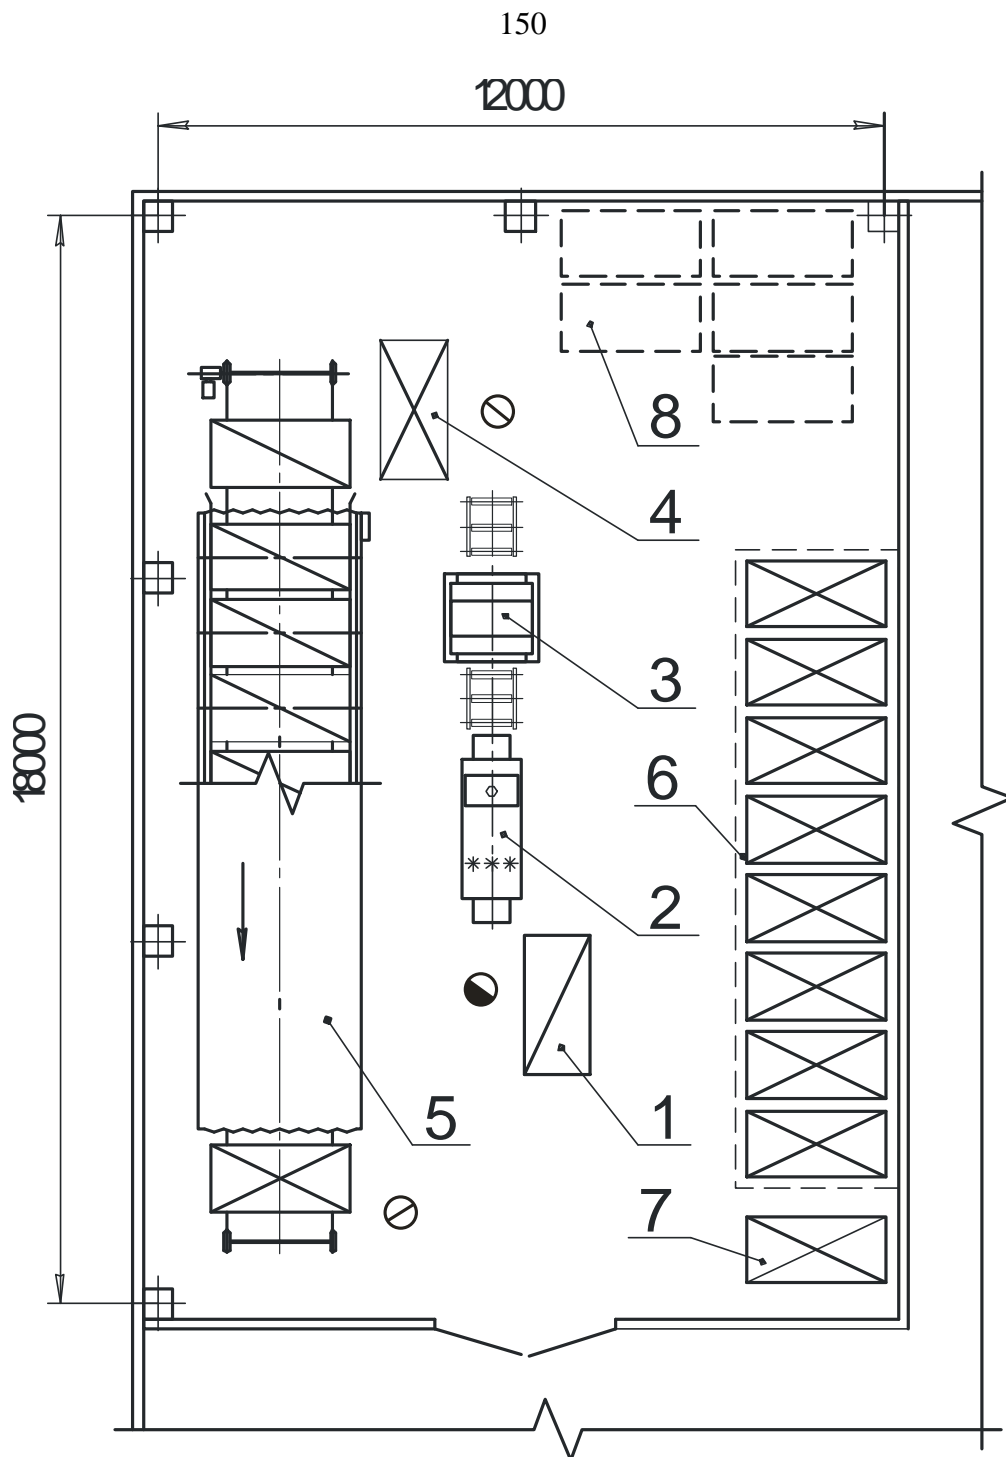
Схема участка отделки при высыхании РЗ ЛКК с конвективной сушкой: 1 – плотный пакет заготовок; 2 – щеточный станок; 3 – вальцовый станок; 4 – этажерка с заготовками; 5 – сушильная камера; 6 – подступное место с вытяжным зонтом; 7 – плотный пакет готовых деталей для отгрузки; 8 – пустые этажерки
